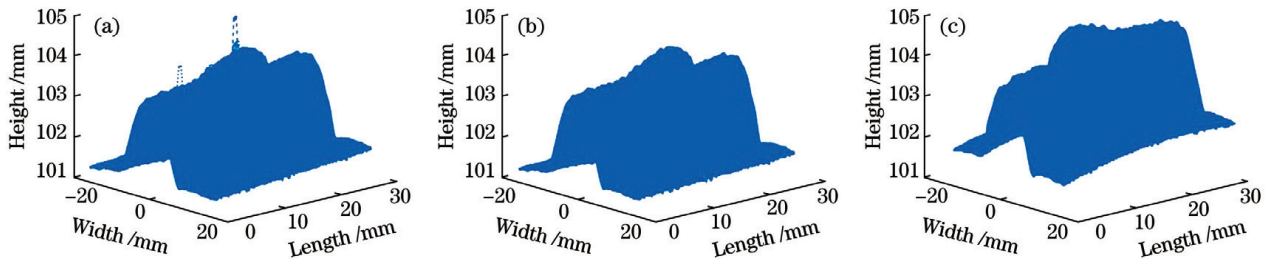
焊缝表面形貌的三维重建。(a)滤波前;(b)滤波后;(c)实际的管道焊缝表面形貌
